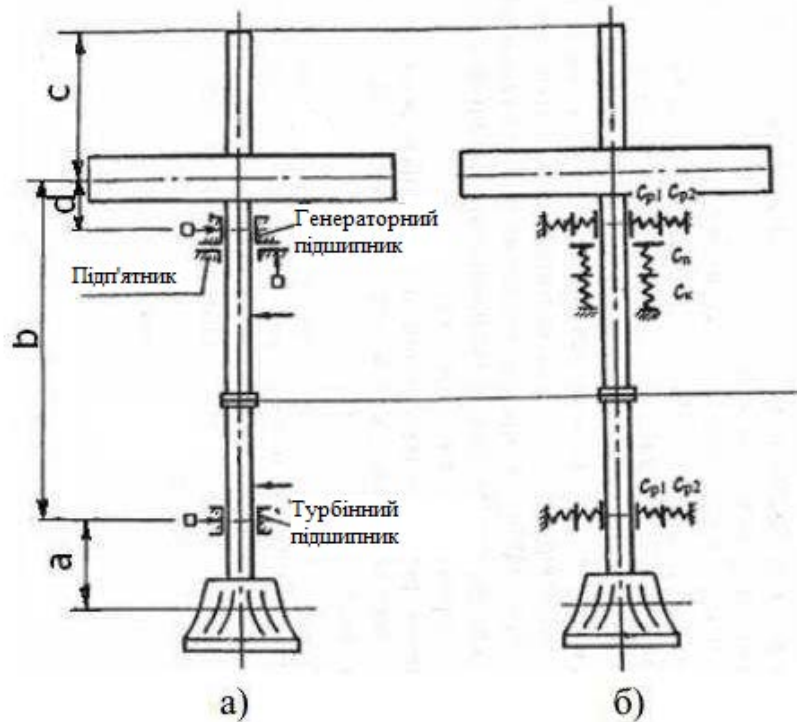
Схема гідроагрегату з пружними зв'язками:
